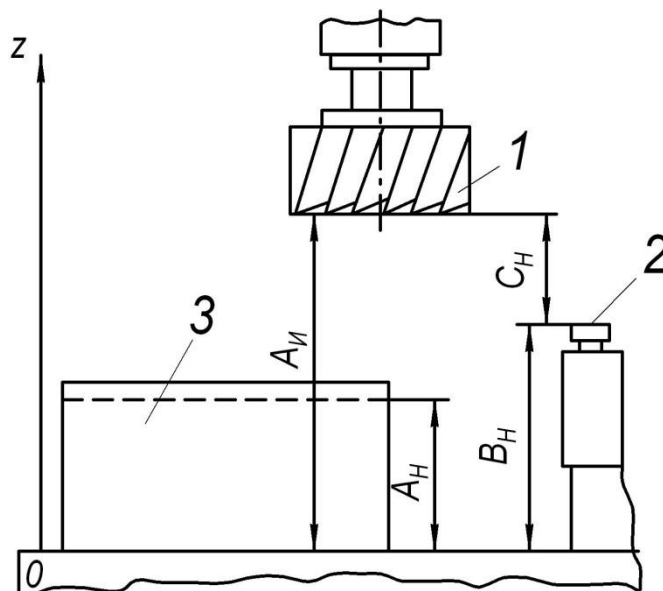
Схема размерной настройки инструментов многоцелевого станка с ЧПУ по оси Z
